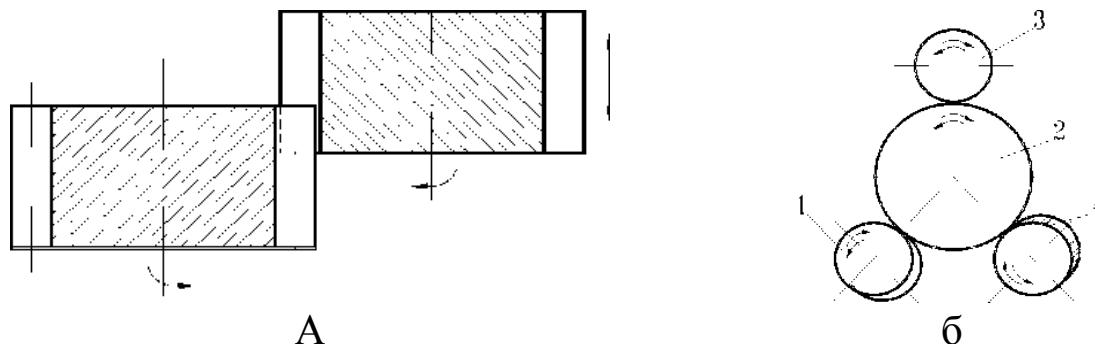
Схемы притирки зубьев зубчатых колёс:
